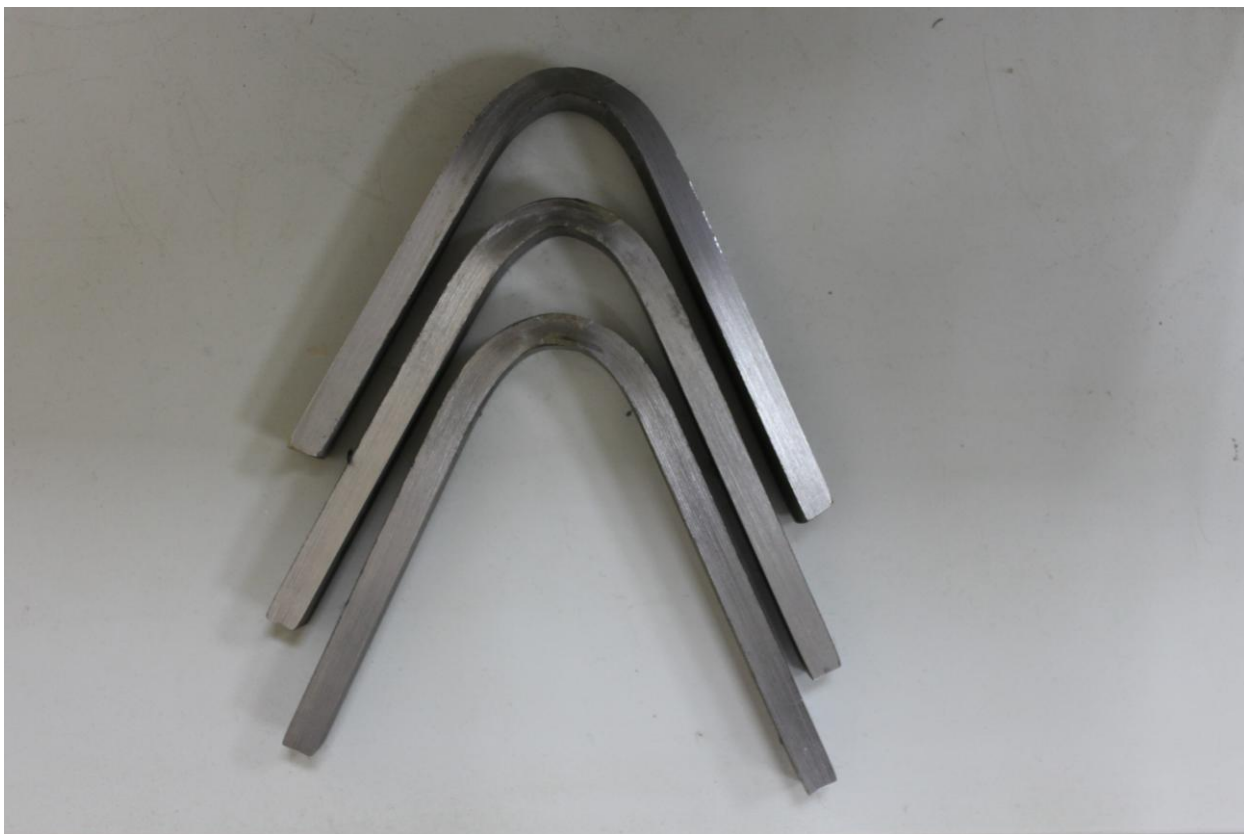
Внешний вид образцов после испытаний на статический изгиб
